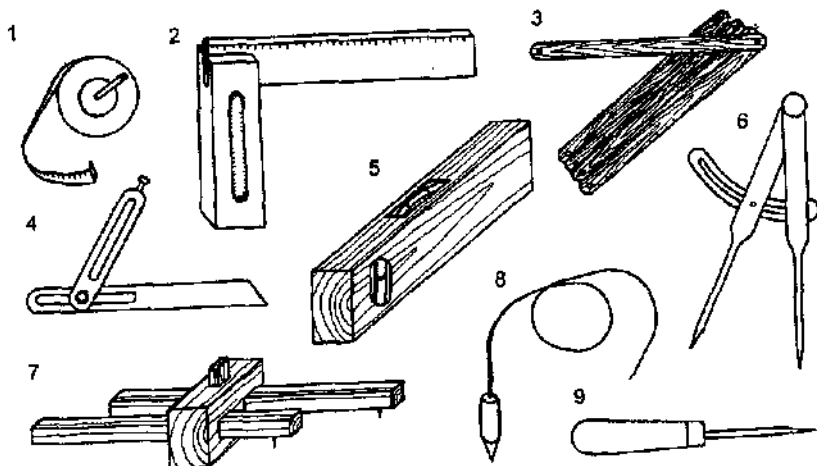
Инструмент для разметки древесины: 1 — рулетка; 2 — угольник; 3 — складной метр; 4 — малка; 5 — уровень; 6 — циркуль; 7 — рейсмус; 8 — отвес; 9 — шило
